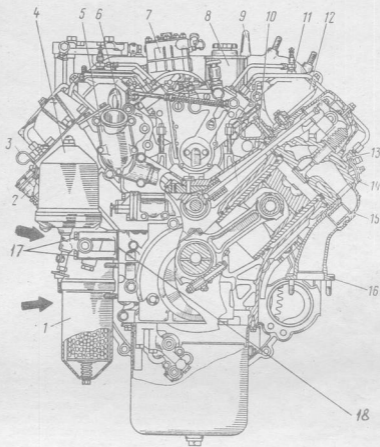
Поперечный разрез двигателя КамАЗ-740.
